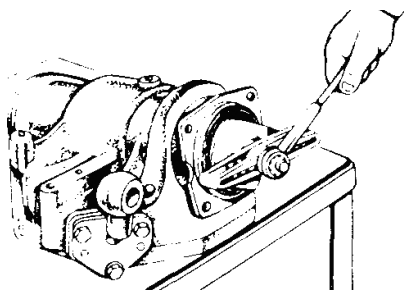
Запрессовка гильзы шкворня в корпус редуктора конечной передачи в сборе.
